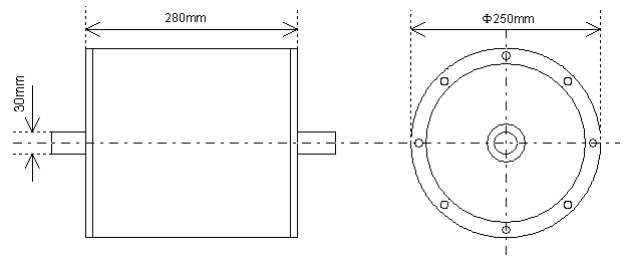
Dimensions hors tout du moteur asynchrone discoïde 2x15 kW
